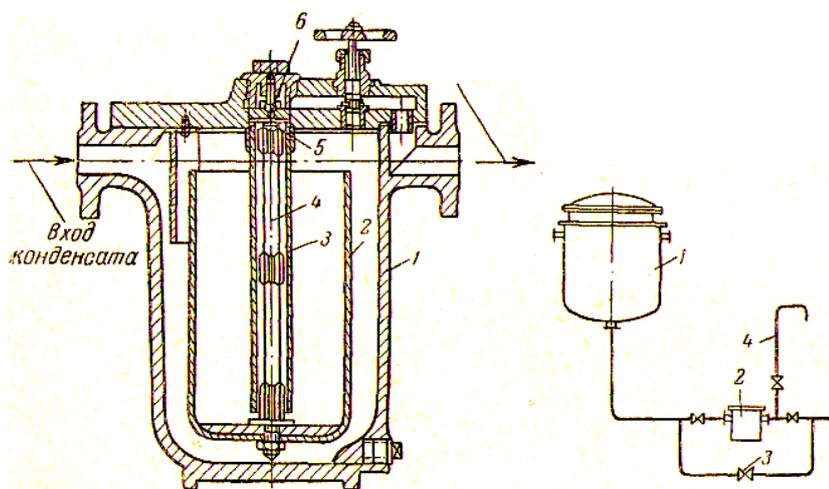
Конденсационный горшок с открытым поплавком: 1-корпус; 2-поплавок; 3-труба; 4- шток; 5-клапан; 6- отверстие для выхода конденсата.
